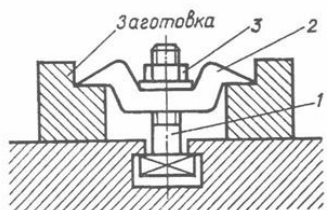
Схема кріплення одночасно двох заготовок:
